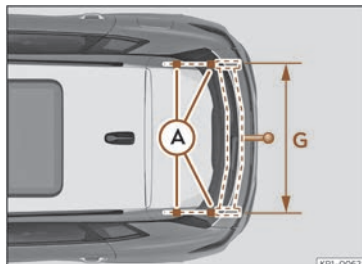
Dispositif d'attelage : cotes et points de fixation.
